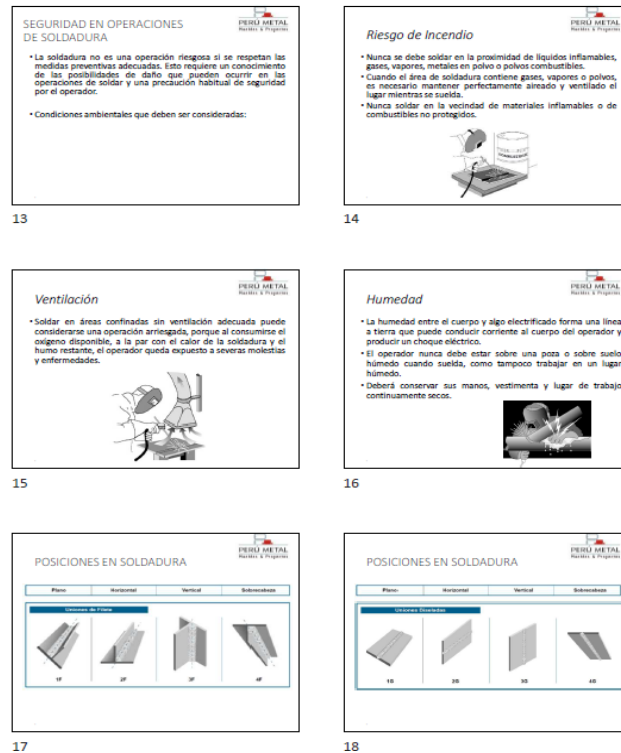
Láminas 13-18 de capacitación sobre técnicas de soldadura Fuente: Elaboración de los autores.
